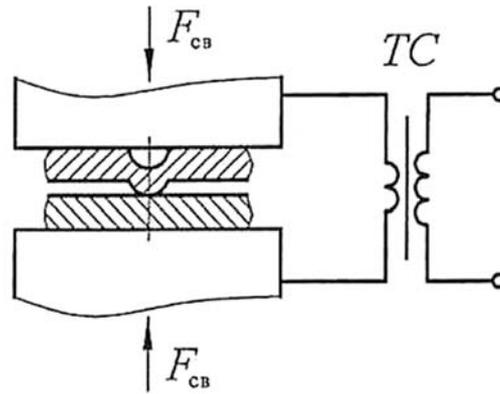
Упрощенная схема процесса контактной рельефной сварки
